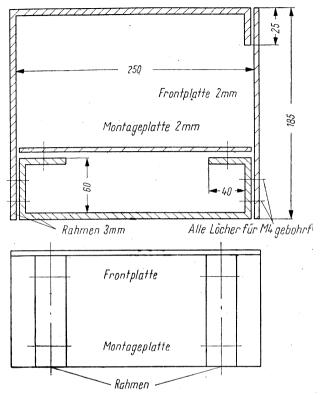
Universalchassis, bei dem Frontplatte und Aufbauchassis durch zwei Rahmen gehalten werden
